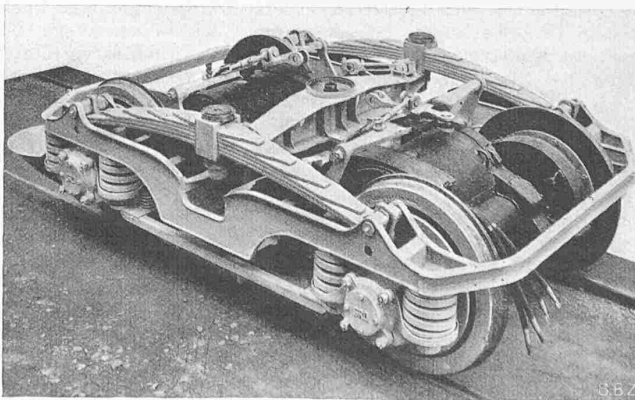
Drehgestell zu 351, Bauart Schlieren, elektr. Ausrüstung MFO
